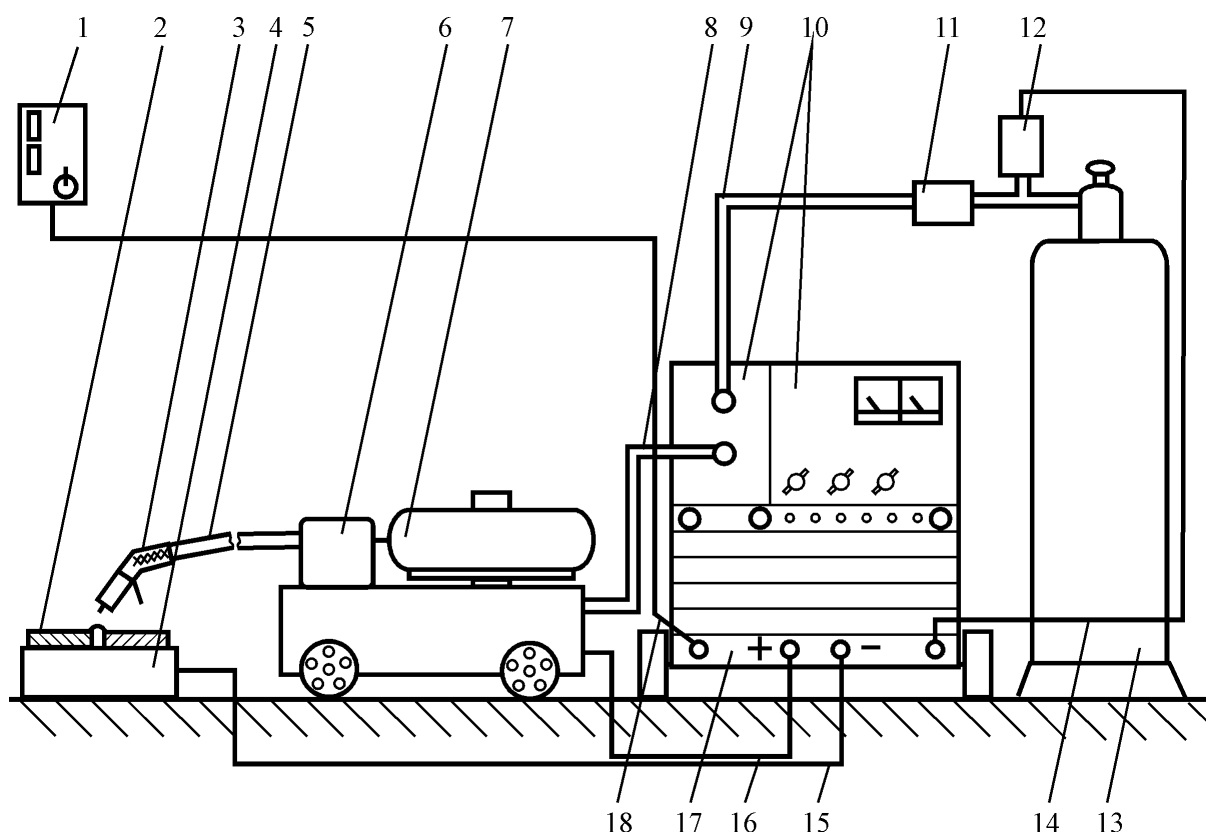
Полуавтомат ПДГ-601: 1 – пульт дистанционного управления; 2 – изделие; 3 – сварочная горелка; 4 – стол; 5 – шланг для подачи сварочной проволоки и углекислого газа; 6 – механизм подачи электродной проволоки; 7 – бухта электродной проволоки; 8, 9 – шланги подачи углекислого газа; 10 – блок управления полуавтоматом; 11 – осушитель углекислого газа; 12 – электроподогреватель углекислого газа; 13 – баллон с жидкой углекислотой; 14 – кабель электропитания подогревателя; 15, 16 – сварочные кабели; 17 – сварочный выпрямитель ВДГ-601; 18 – кабель подключения пульта дистанционного управления
